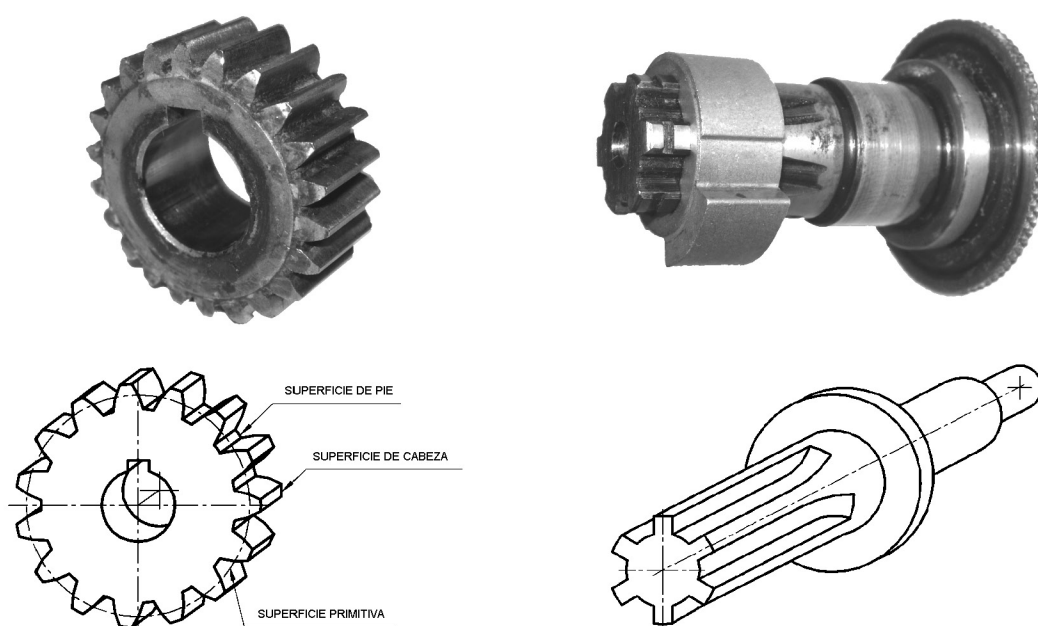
Dientes (izquierda) y acanalados (derecha)
